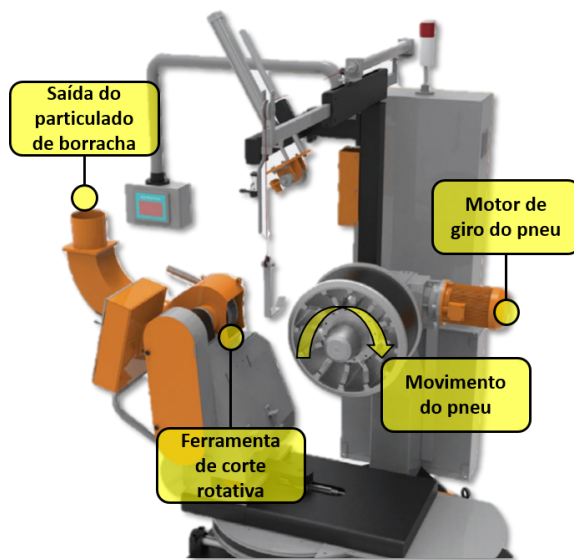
Equipamento para remoção de borracha durante a recapagem de pneus.
